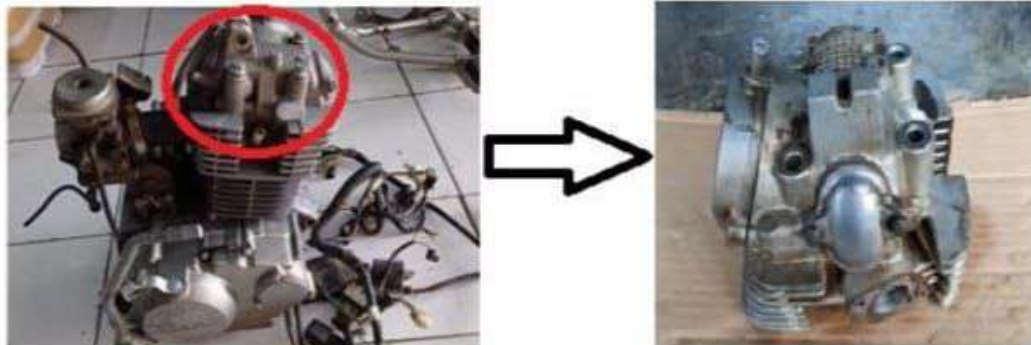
Skema Alur Disassembly Head Silinder Mesin Sepeda Motor KLX 150
